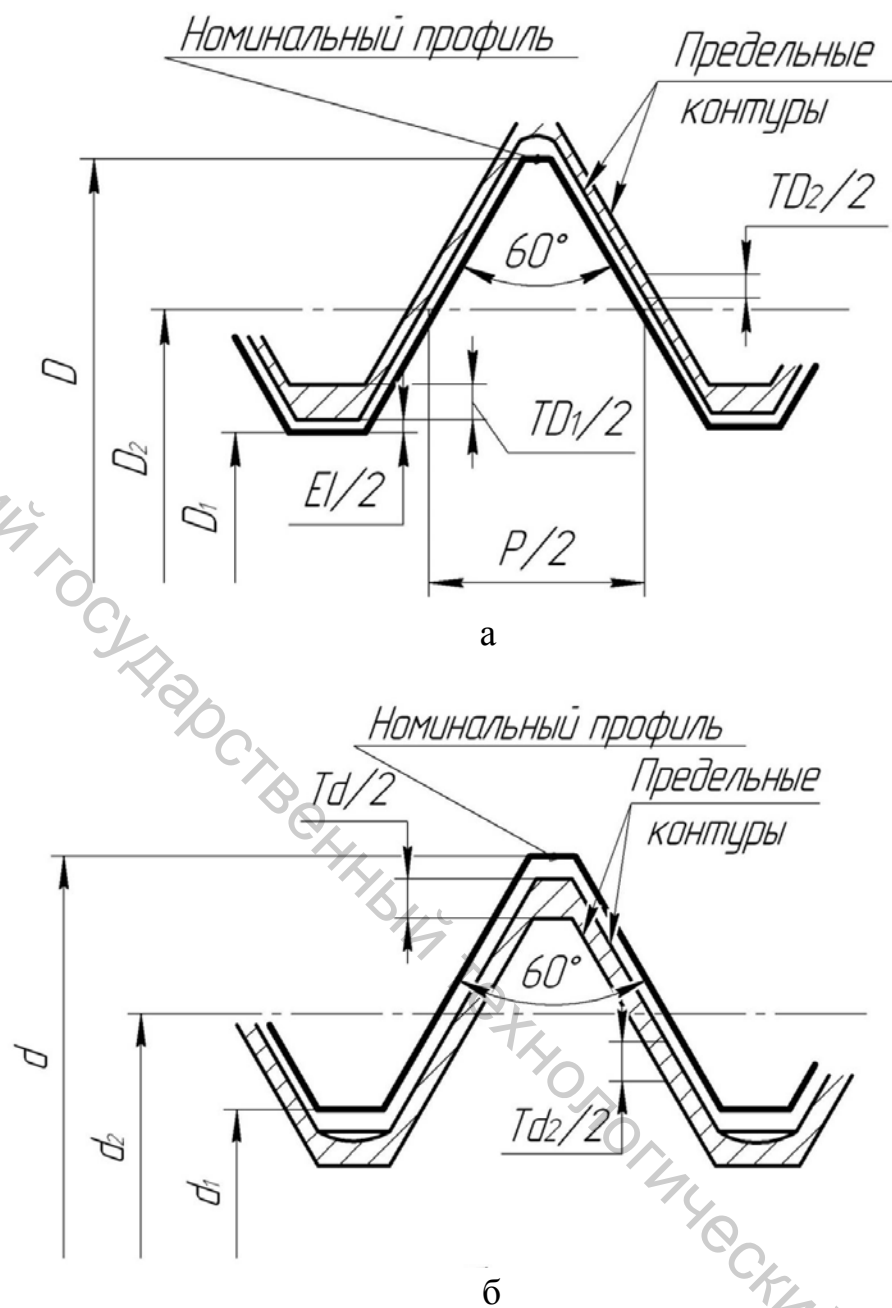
Положение полей допусков для резьбы с зазором:
